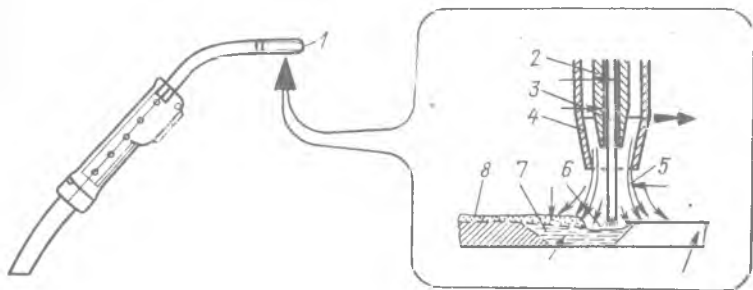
Схема сварочного процесса в защитном газе:
